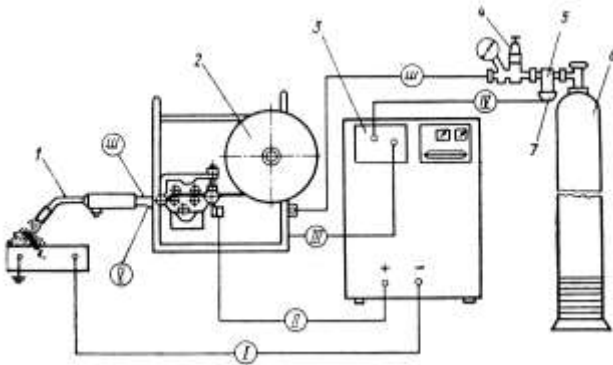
Схема установки для напівавтоматичного зварювання і наплавлення в середовищі вуглекислого газу: 1 – паличник зварювальний; 2 – механізм подаючий; 3 – джерело живлення; 4 – редуктор; 5 – осушувач; 6 – балон з вуглекислим газом; 7 – підігрівач; I-IV – з'єднувальні кабелі; Ш – шланги
